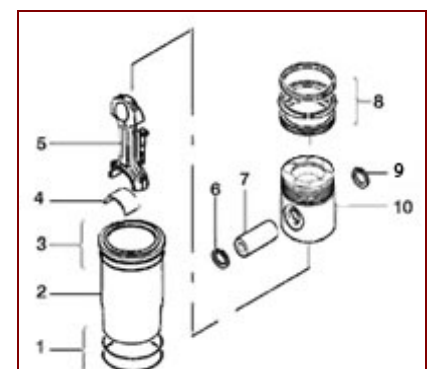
Разборка кривошипно-шатунного механизма
